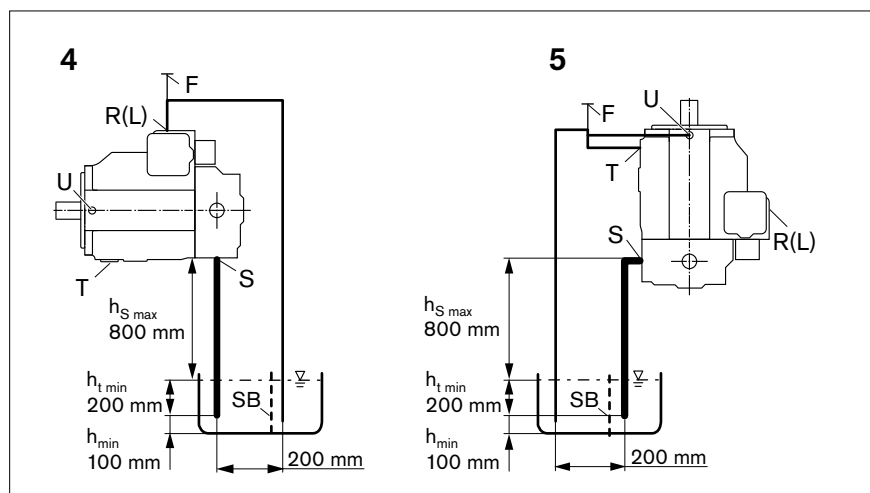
Übertankeinbau mit waagrechter Einbaulage 4 und senkrechter Einbaulage 5
